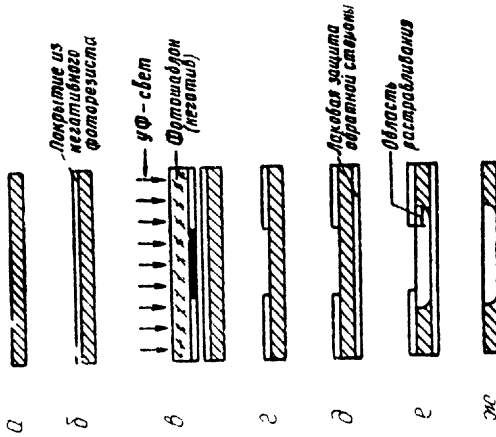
Схема фотохимического способа изготовления масок: а — подготовка; б — нанесение фоторезиста; в — экспонирование; г — проявление; д — нанесение лаковой защиты; е — травление; ж — готовая маска после удаления лаковой защиты
